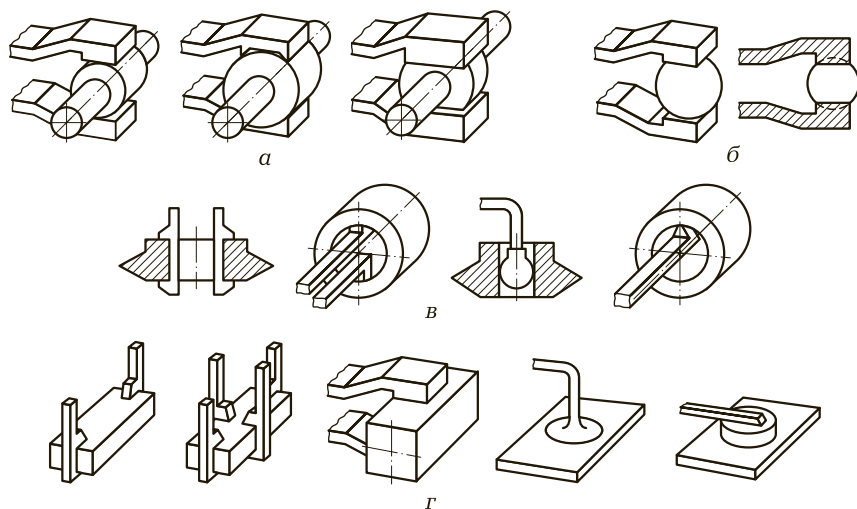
Зажимные губки для цилиндрической (а), шаровой (б), внутренней цилиндрической (в) и плоской (г) поверхностей
